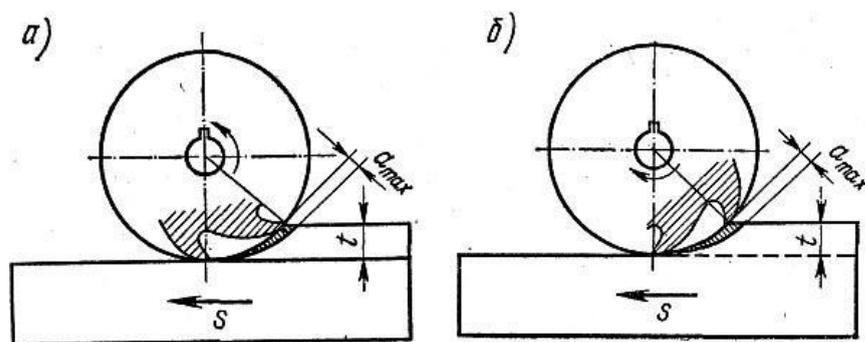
Схеми фрезерування: а – зустрічне; б – попутне
